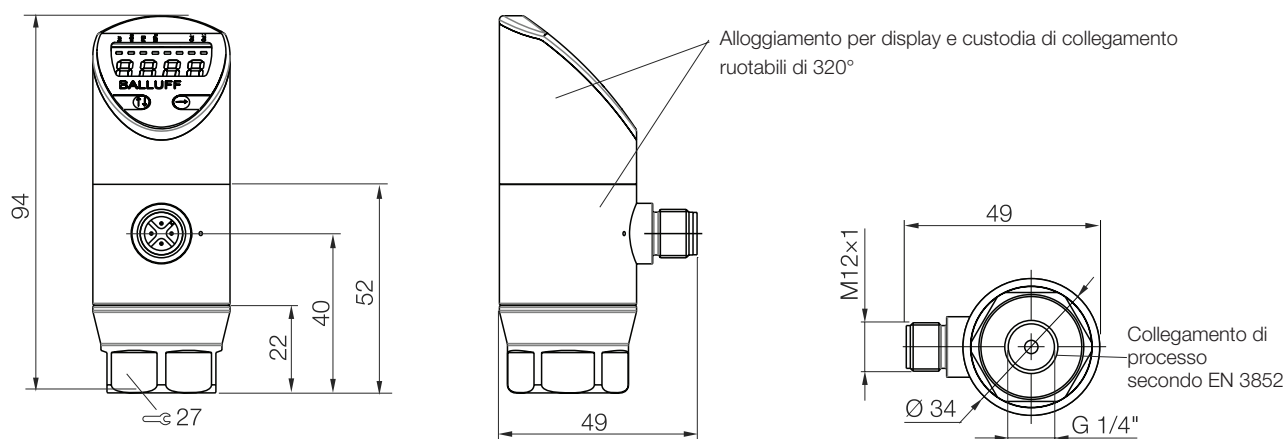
Disegno quotato sensore di pressione standard e High-End, non a filo sul lato frontale
